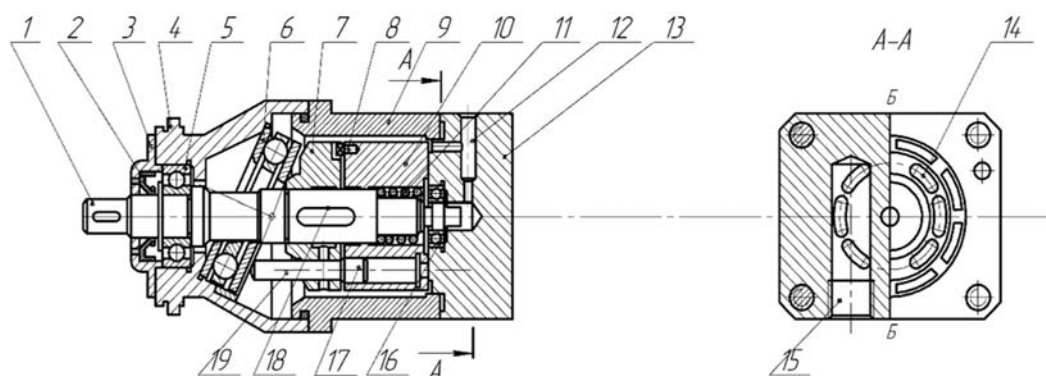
Конструкция аксиально-поршневого гидромотора
